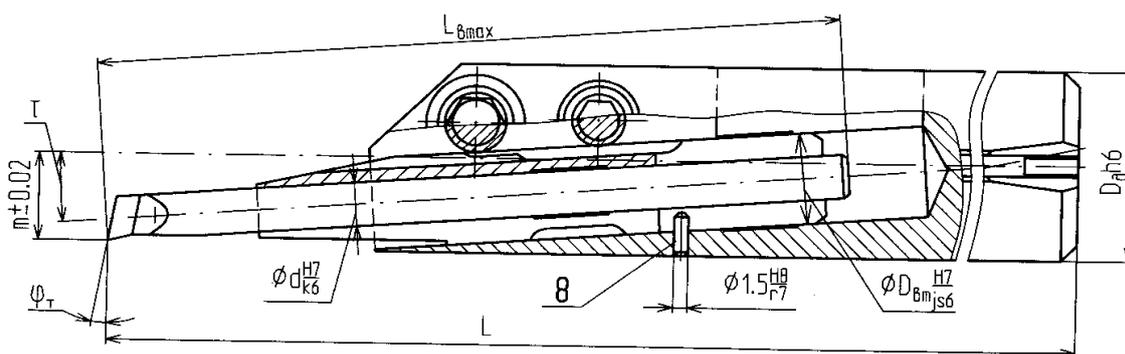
Резец унифицированный универсальный расточной контурный для обработки диапазона диаметров и подрезки торцевой поверхности глухого отверстия.
